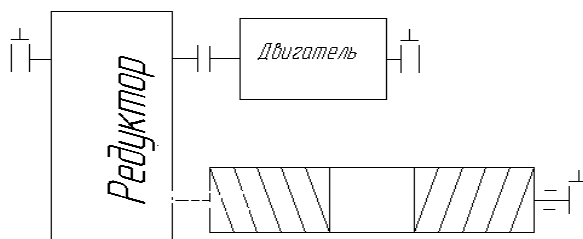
Предлагаемая кинематическая схема механизма подъема
